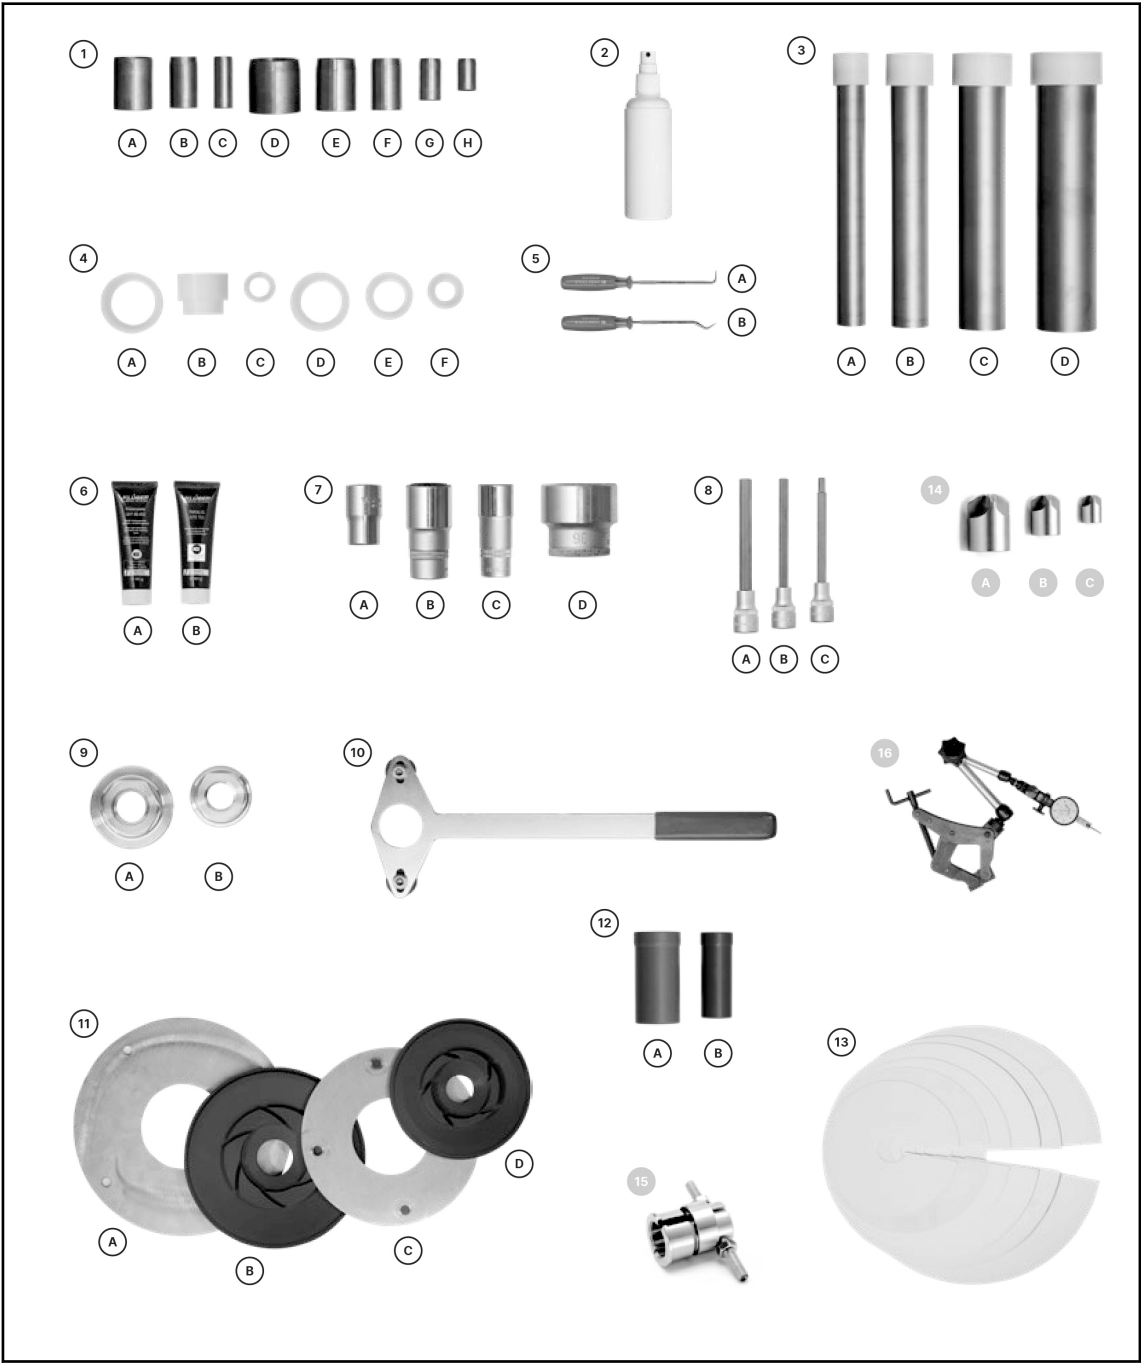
Werkzeuge im GEA Hilge Montagekoffer
